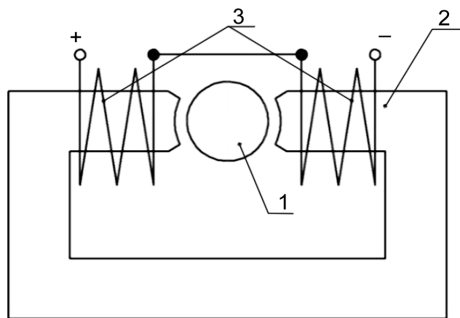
Схема взаимного расположения цилиндрической поверхности и электромагнитов:
